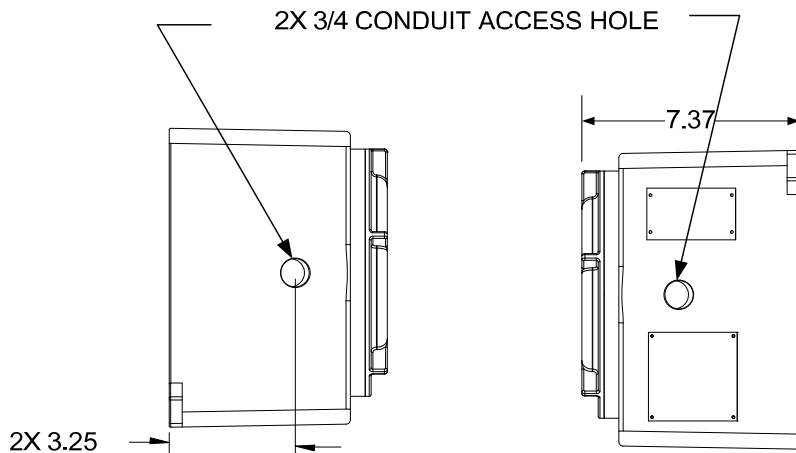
Dimensões laterais da fonte de alimentação CA à prova de explosão
